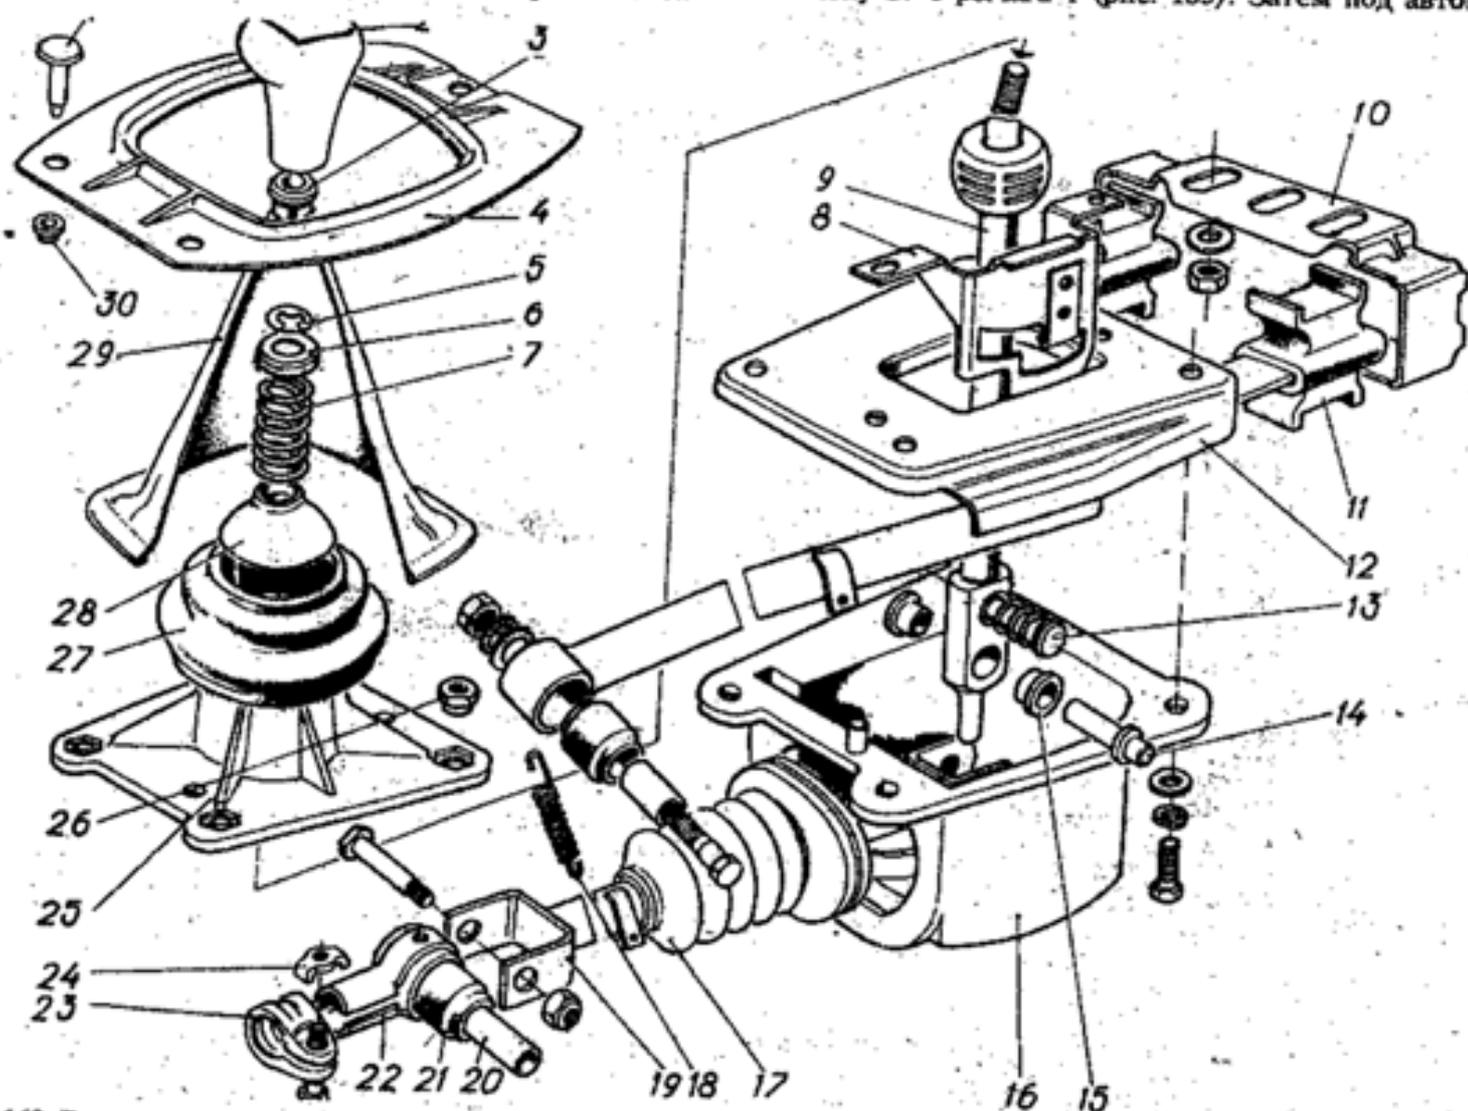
Детали привода управления механизмом переключения передач: 1 - пистон; 2 - рукоятка рычага; 3 - втулка; 4 - крышка чехла; 5 - кольцо стопорное; 6 - шайба опорная; 7 - пружина; 8 - кронштейн упора; 9 - рычаг переключения передач; 10 - кронштейн наружный; 11 - муфта крепления основания; 12 - основание привода; 13 - упор подвижный с пружиной; 14 - упор направляющий; 15 - втулка опорная; 16 - крышка привода; 17 - чехол защитный; 18 - пружина возвратная; 19 - вал управления; 20 - втулка внутренняя; 21 - втулка амортизационная; 22 - втулка шарнира вала управления; 23 - хомут стяжной; 24 - гайка хомута; 25 - опора шаровая; 26 - гайка опоры; 27 - уплотнитель привода; 28 - чашка; 29 - чехол привода; 30 - втулка пистона.
